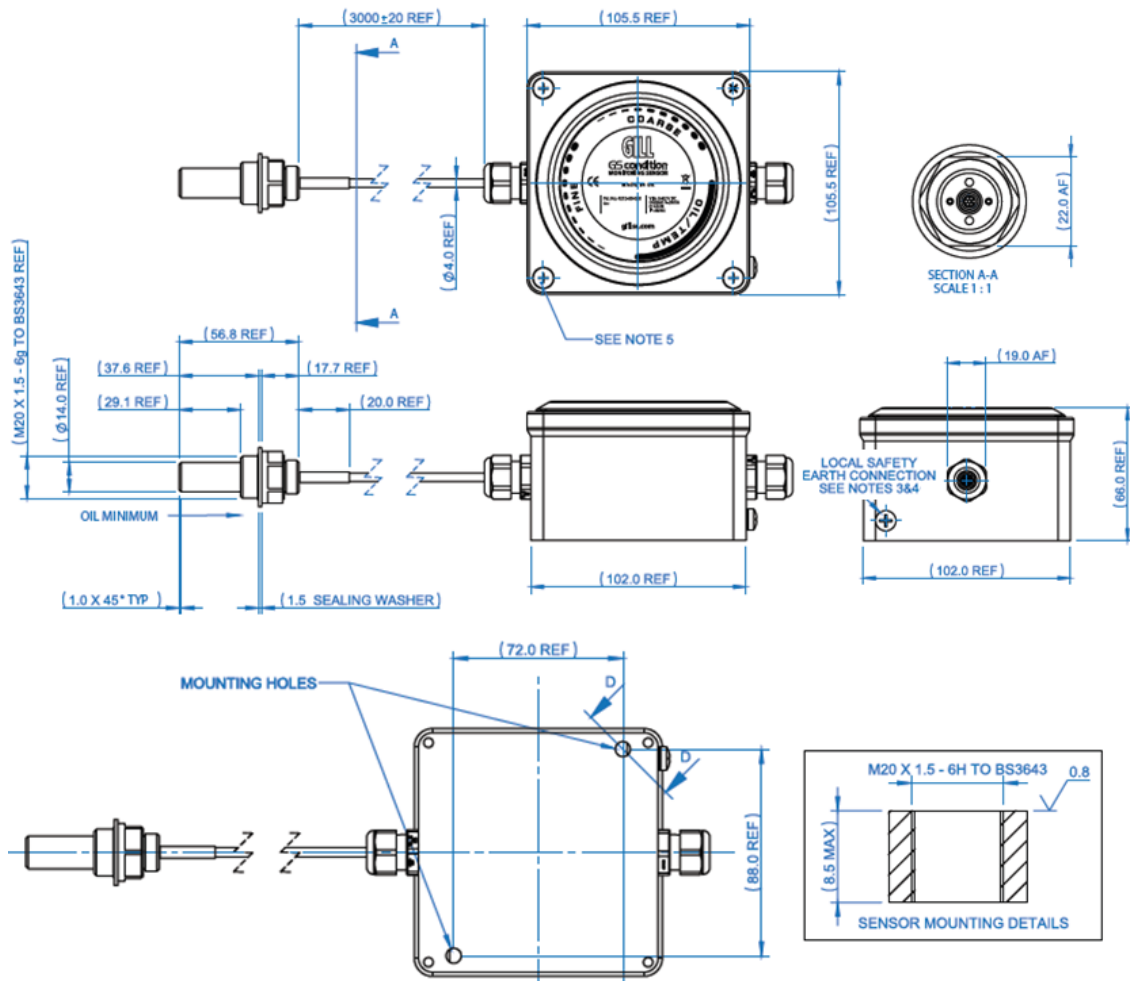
Especificaciones mecánicas del sensor Gill 2.
